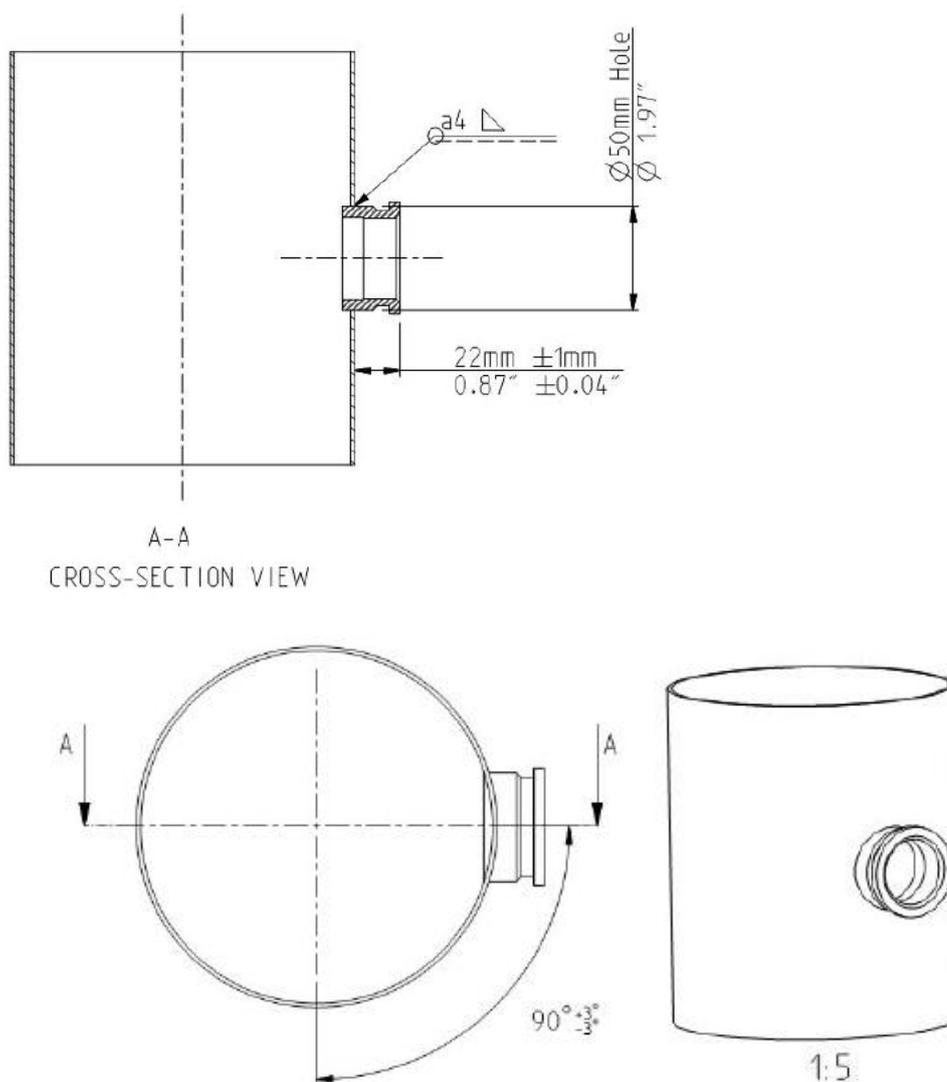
Instrução de soldadura de acoplamento de processo para processar tubo PN10.
